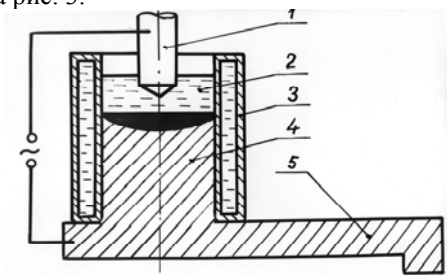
Схема наплавлення: 1 – витратний електрод; 2 – флюс; 3 – мідний водоохолоджуваний кристалізатор; 4 – наплавлена частина; 5 – деталь.
